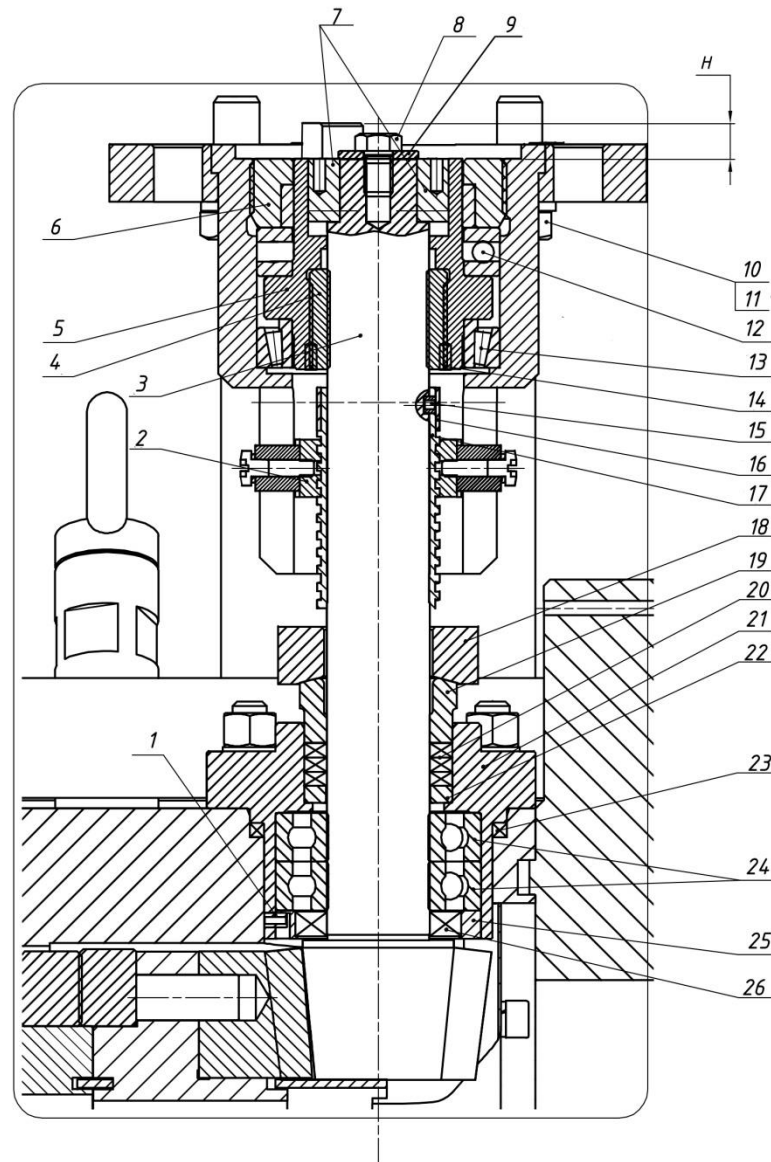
Сборочный чертеж (габаритный 1:10) ходового узла [Assembly drawing (overall 1:10) of motion gear]
